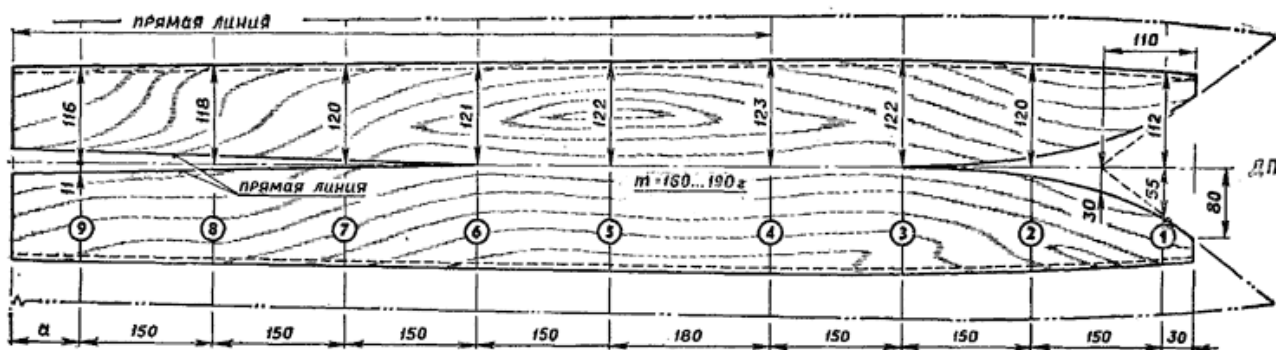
Основные размеры раскрой листа фанеры для изготовления корпуса (размер «а» определить после сборки корпуса, линией условного контура показаны размеры ранее применявшейся выкройки).
